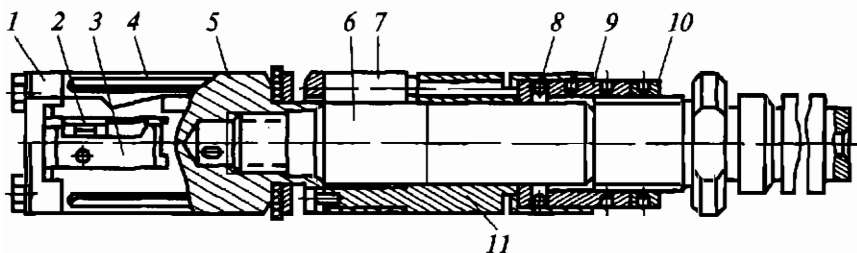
Комбинированный инструмент для растачивания и раскатывания стальных гидроцилиндров:
